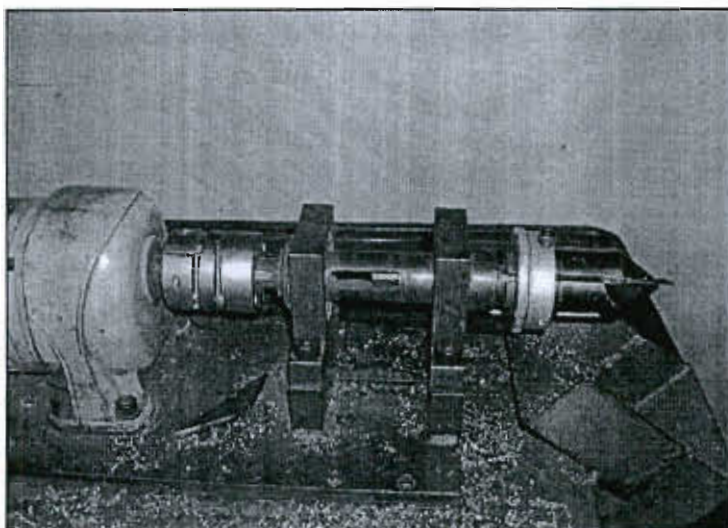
เครื่องเชื่อมและขึ้นรูปท่อสแตนเลส (Pipe Forming & Welding M/C)
